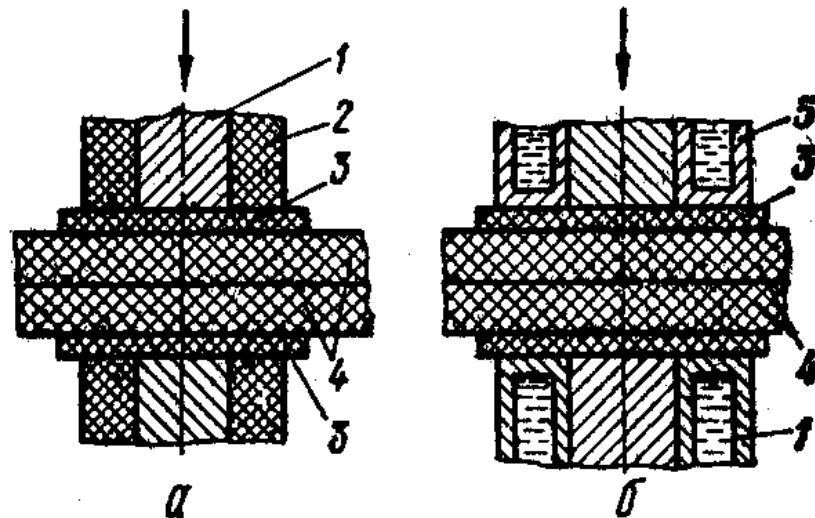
Схема пресового зварювання (а-без охолодження; б-з охолодженням): 1-нагрівник; 2-теплоізоляційна пластина; 3-прокладка; 4-виріб; 5-охолоджувач.
